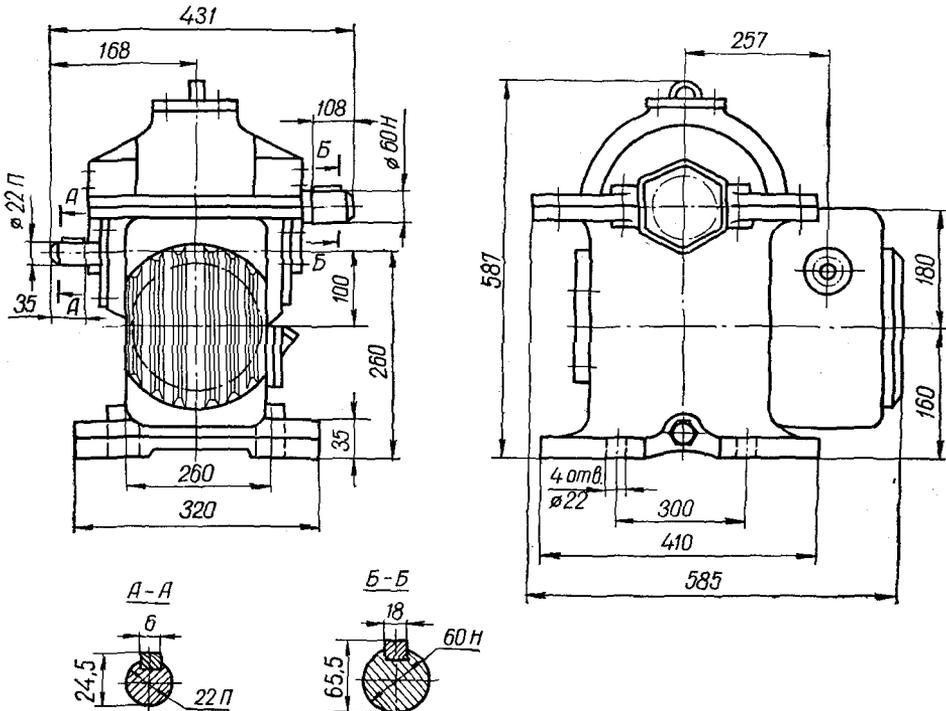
Основные и габаритные размеры редуктора ЧДПМ 100/180.
